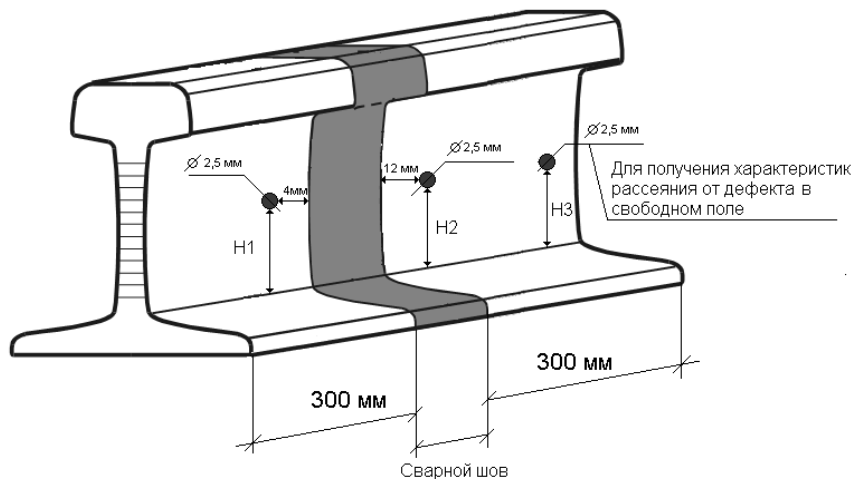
Экспериментальный образец сварного стыка рельса с искусственными дефектами вблизи сварного шва
